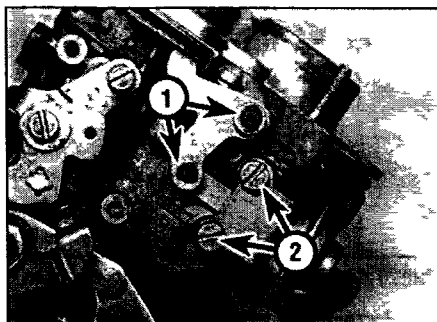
Снимите фиксаторы (1) и отсоедините поворотный рычаг вакуумного привода от крышки карбюратора
